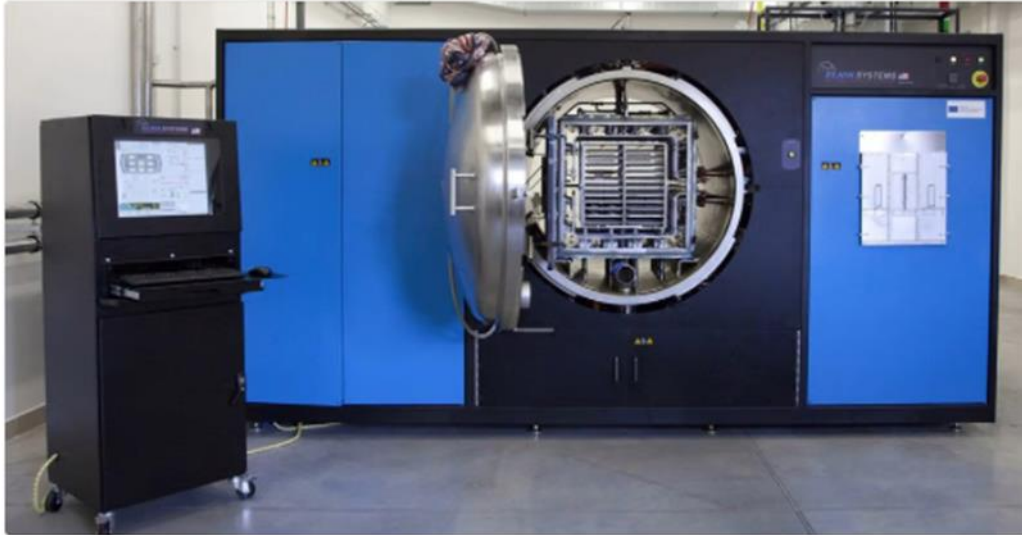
Impresora 3D - 6. Sinterizado Láser Directo en Metal - Fuente: All3DP
